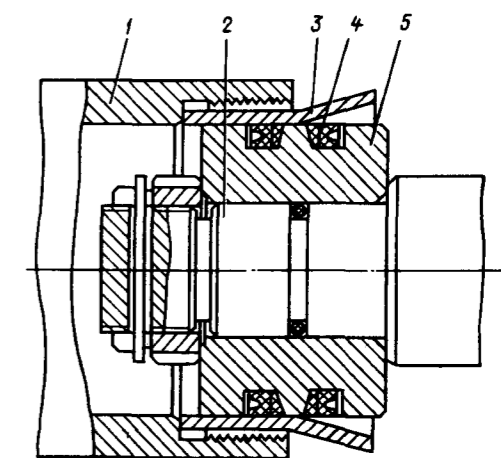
Приспособление для монтажа поршня в гидроцилиндр I типа:
